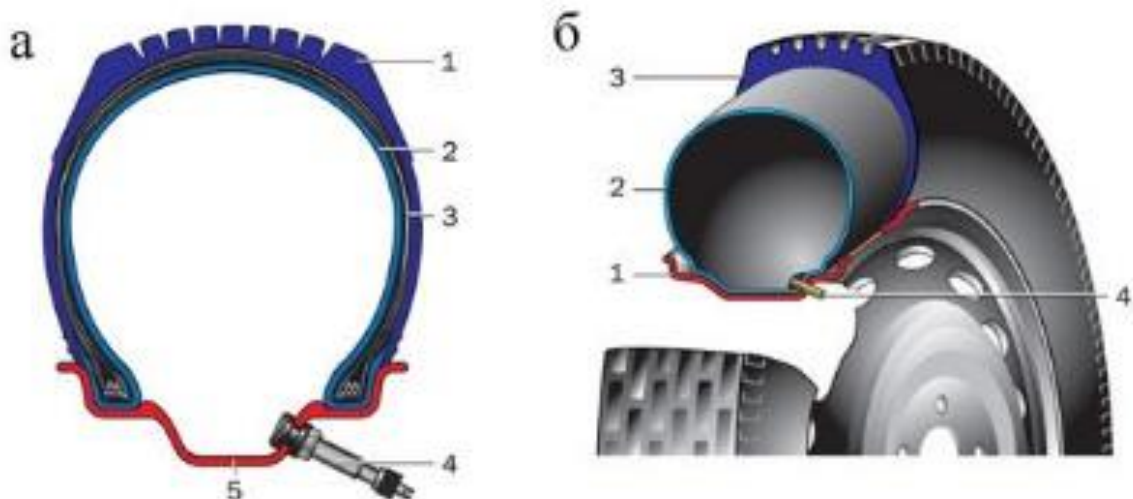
Конструкція колеса (а) з безкамерною шиною:
